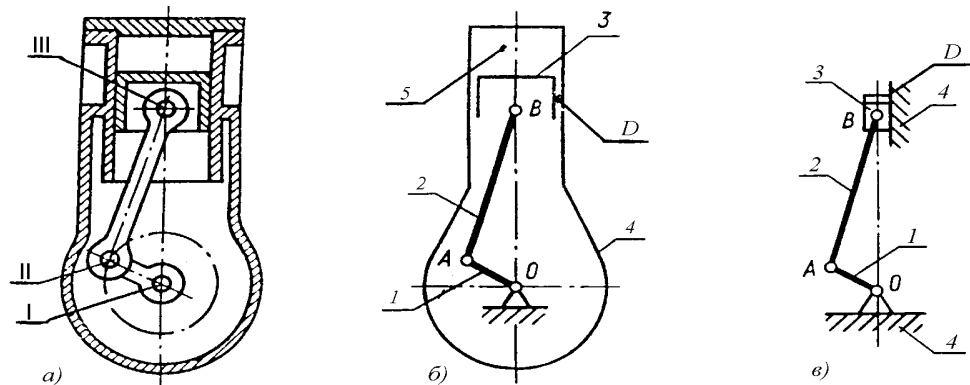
Кривошипно-шатунний механізм компресора (двигуна внутрішнього згорання):
